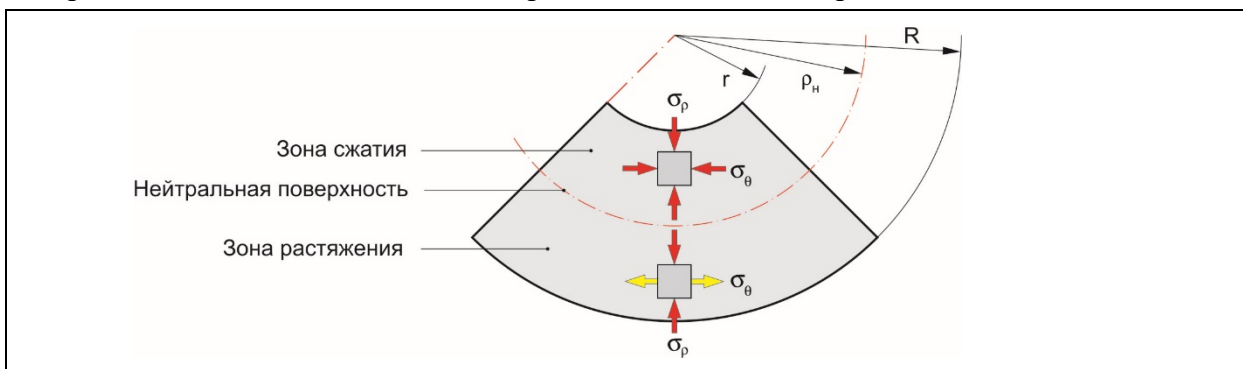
Схема напряженного состояния заготовки при изгибе.
